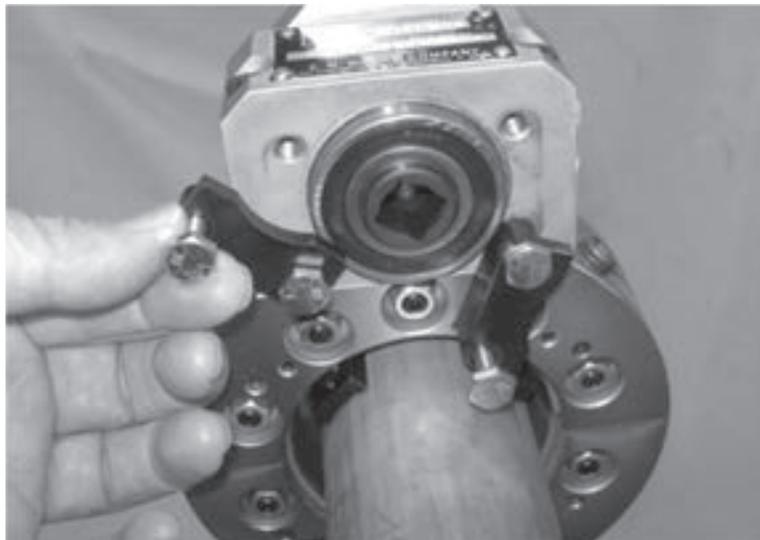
Entfernen Sie die Zylinderkopfschrauben der Motorspanner und montieren Sie Sechskantschrauben, um eine SDSF mit Druckluftantrieb auf einen Elektroantrieb umzurüsten.
